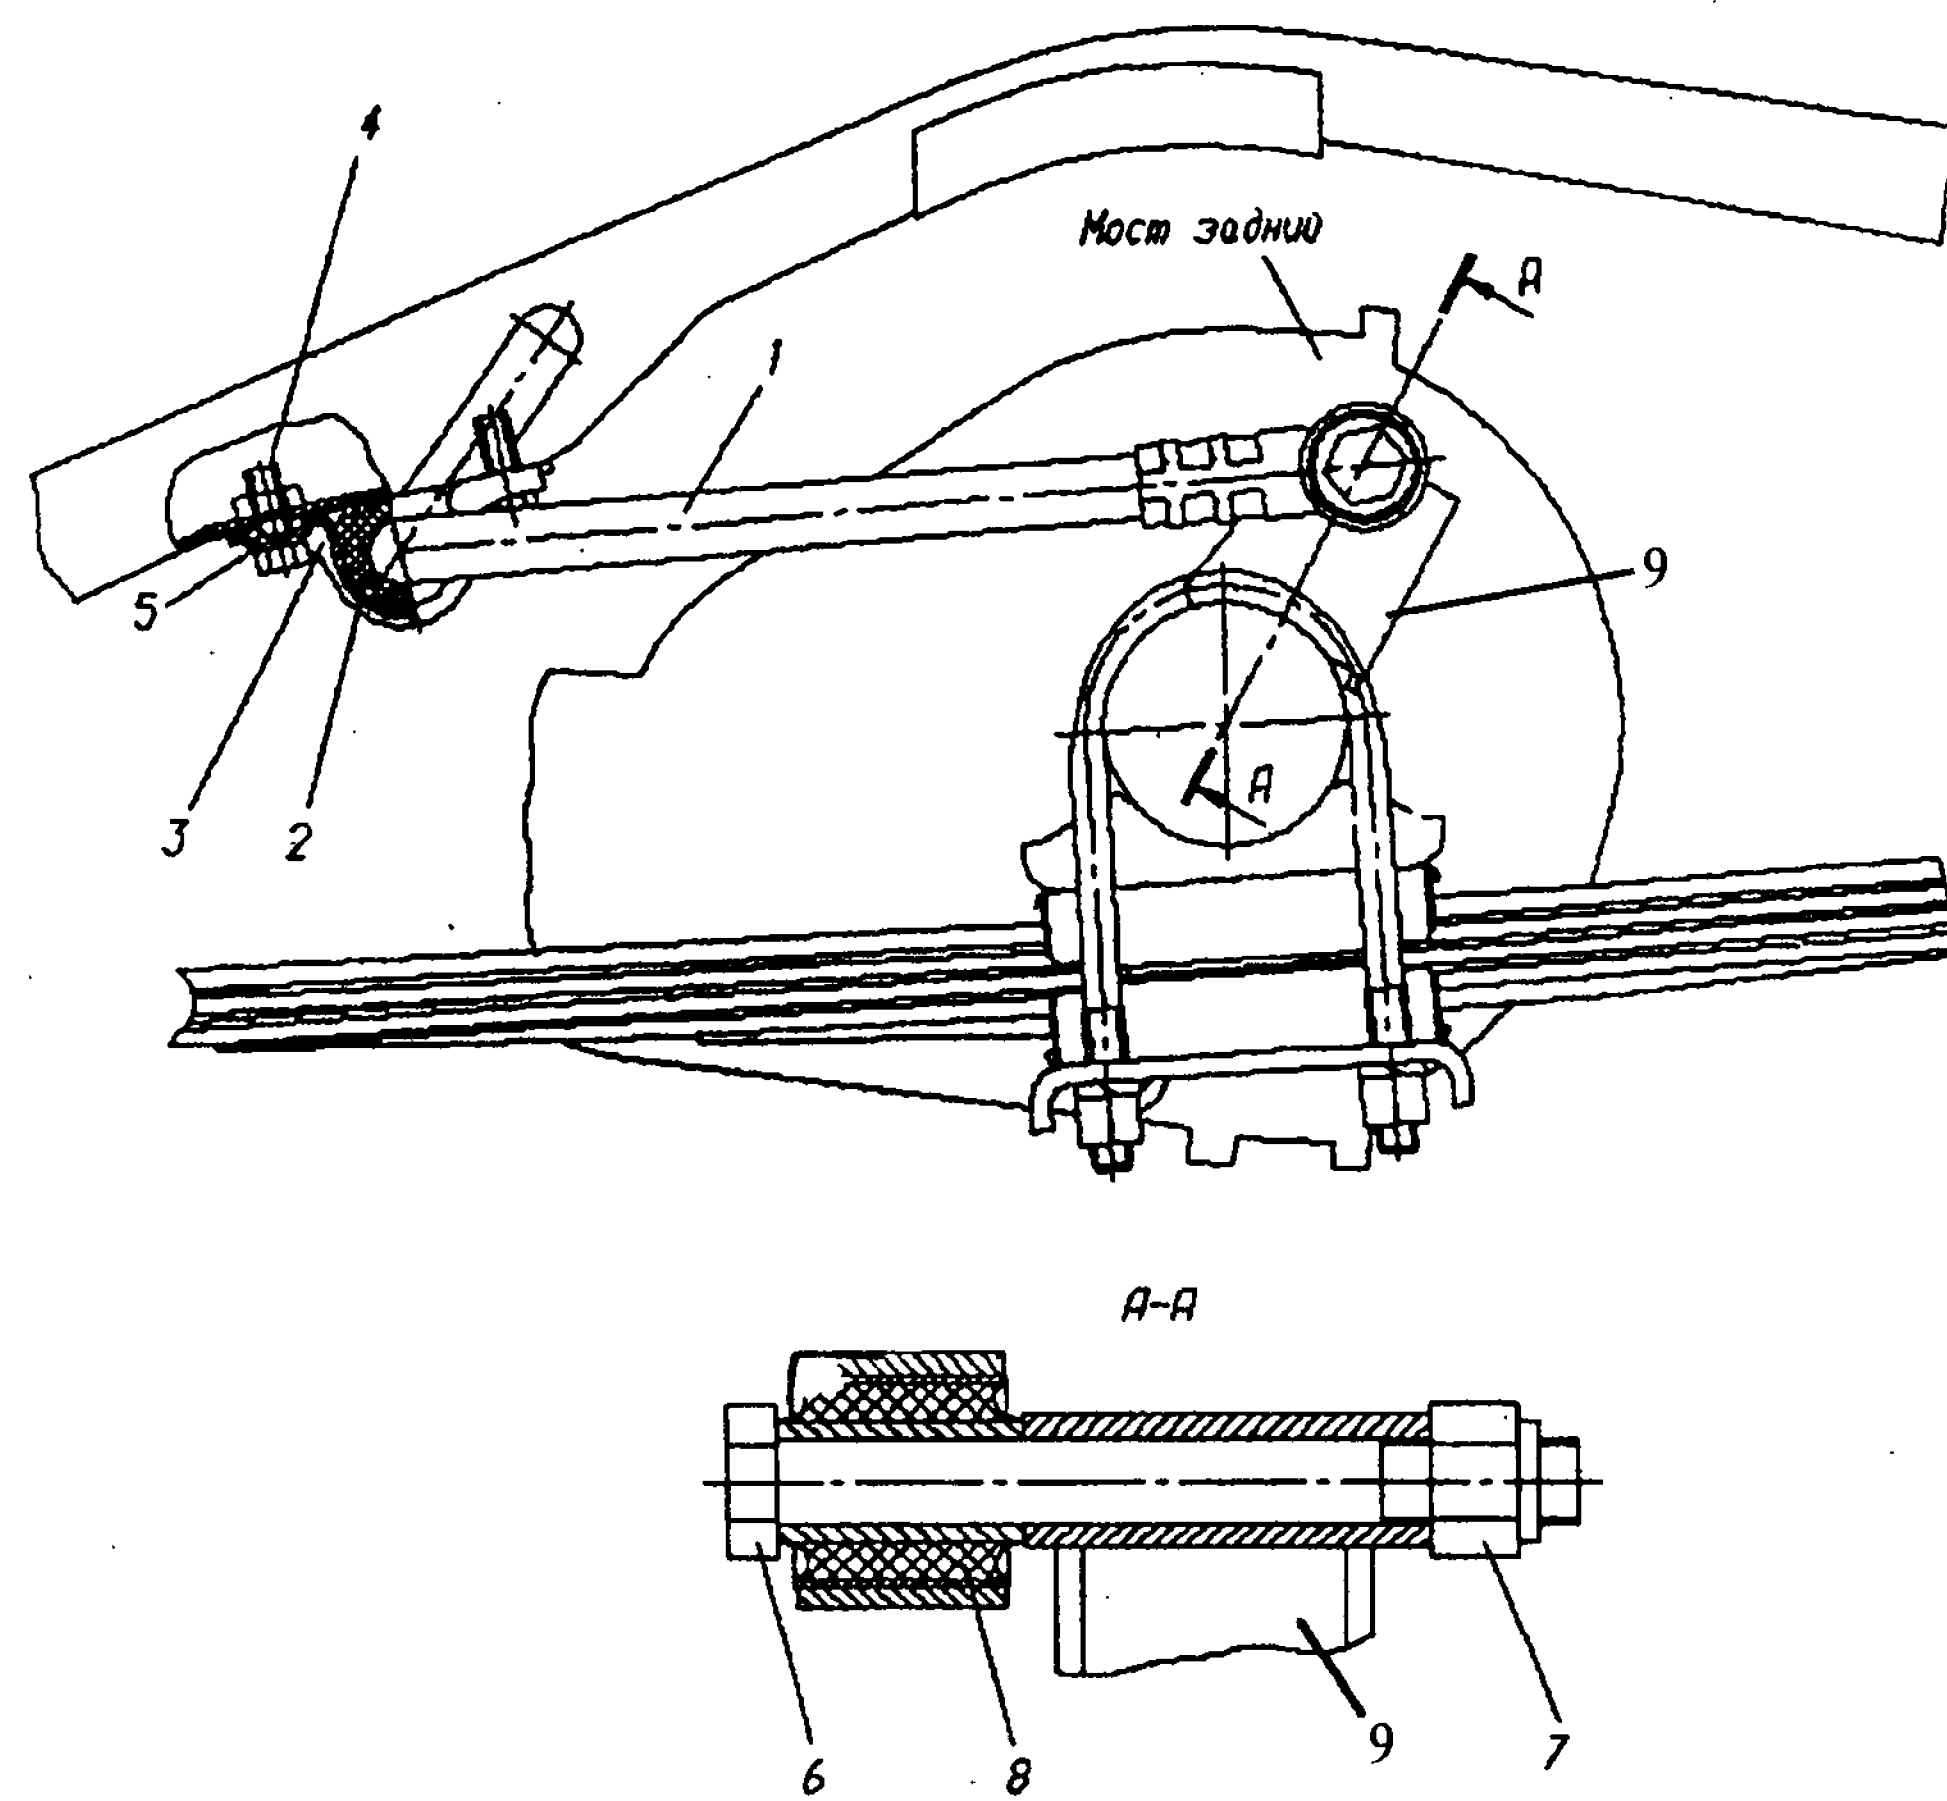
Стабилизатор заднего моста: 1 - штанга стабилизатора; 2 - подушка штанги; 3 - скоба крепления подушки; 4 - болт крепления скобы; 5 - шайба пружинная; 6 - болт крепления конца штанги стабилизатора к кронштейну заднего моста; 7 - гайка болта; 8 - сайлентблок конца штанги стабилизатора; 9 - приварной кронштейн заднего моста
